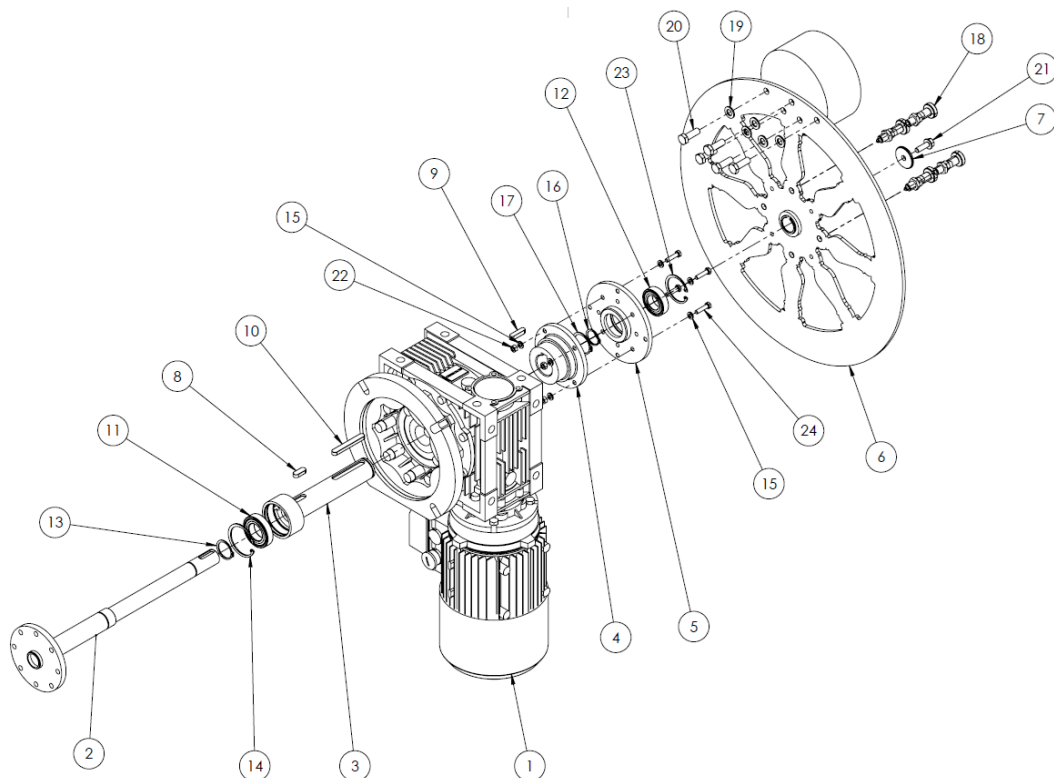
Vista explosionada del muntatge del mecanisme motriu
